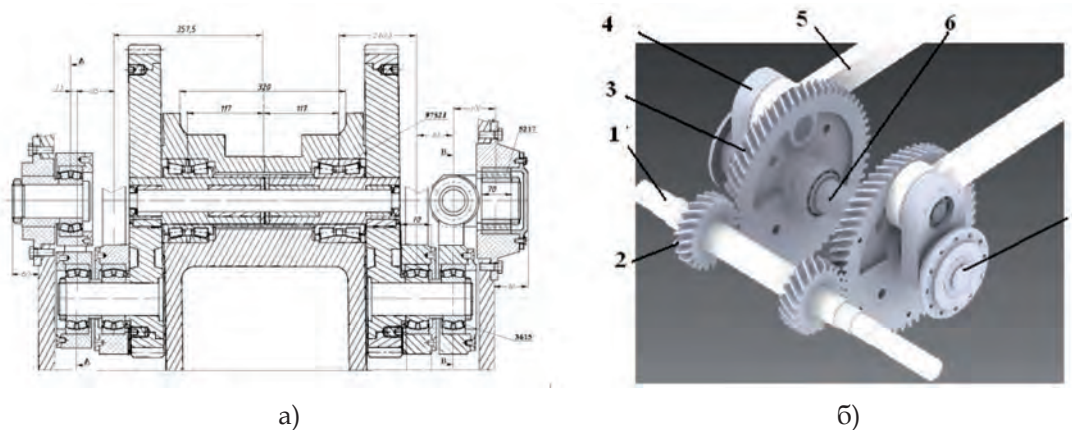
Модернизированный главный привод стана ХПТ 32 с измененным кривошипом и усиленными опорными узлами (дополнительными коленами): 1 – приводной вал; 2 – шестерня приводная; 3 – колесо кривошипное; 4 – колена; 5 – шатун; 6 – раздвоенный вал кривошипного колеса с встроенным торсионом; 7 – крышка станин стана
